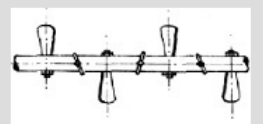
Componentes de un tornillo transportador. Fuente: Ingemecánica.
